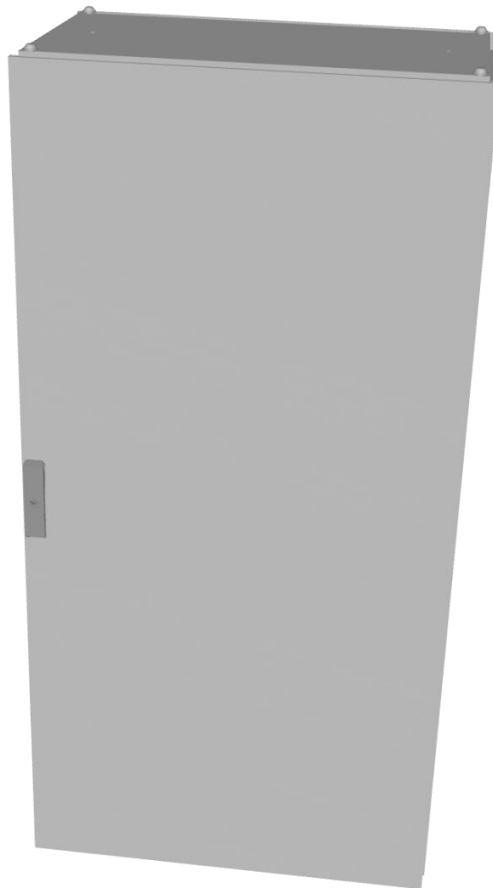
ARMOIRE DE DIMENSIONS H1600xL800xP500 AVEC FERMETURE A CLEF.
